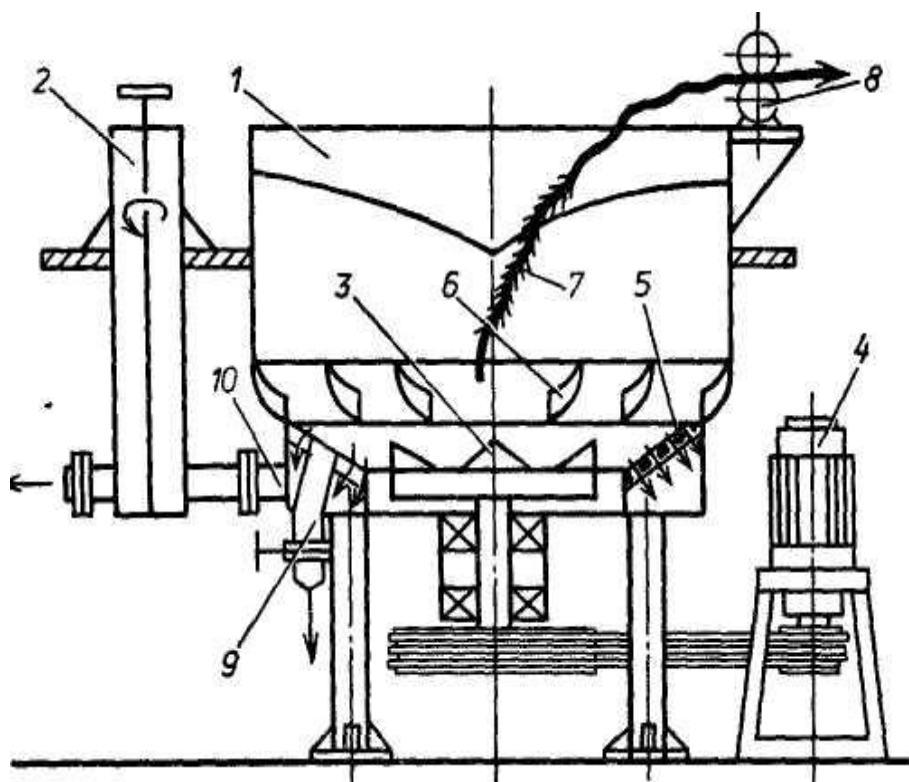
Схема гидроразбивателя открытого типа: 1 - ванна; 2 — переливной ящик; 3 - ротор; 4 - электродвигатель привода ротора; 5 - сита; 6 — неподвижные направляющие лопасти; 7 - жгут; 8 - жгутовытаскиватель; 9 – грязевик для сбора тяжелых загрязнений; 10- выпускной патрубок отвода готовой массы
